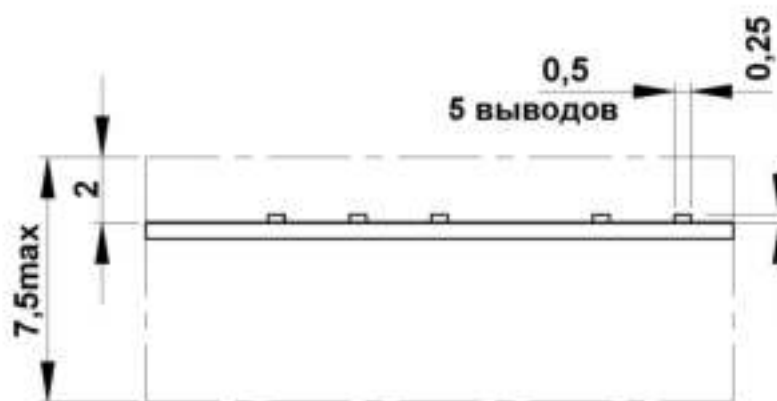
Габаритный чертеж модулей в конструктивном исполнении «Н»
